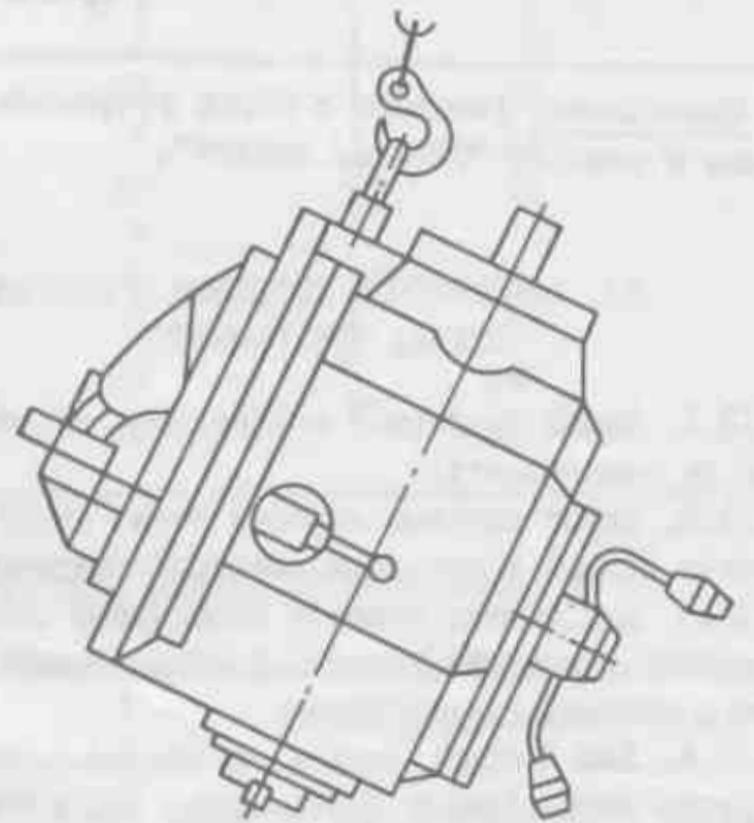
Схема транспортировки шпиндельной головки станка 6Т10
